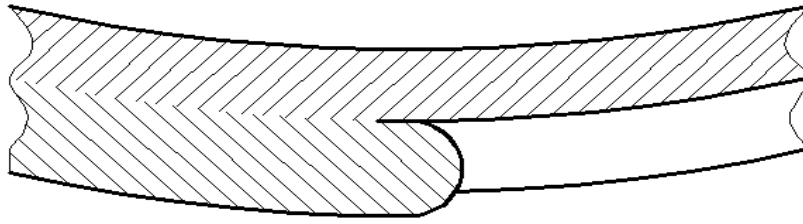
Зовнішній вигляд перетікання металу в області зварювання
